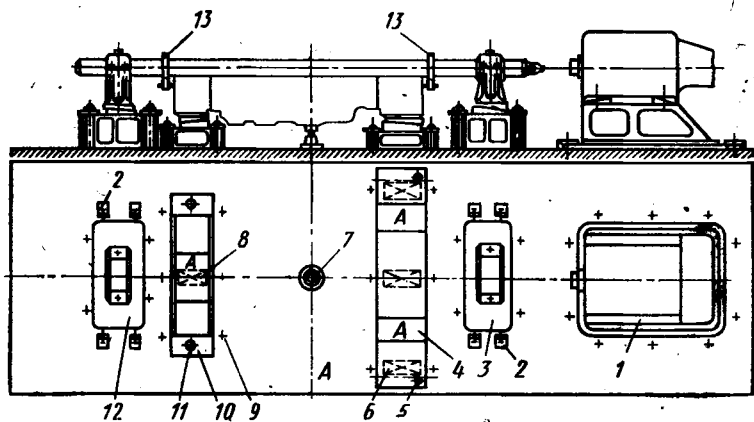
План расположения оснастки для обработки корпуса турбины типа ВКТ-100 на расточном стенде:
